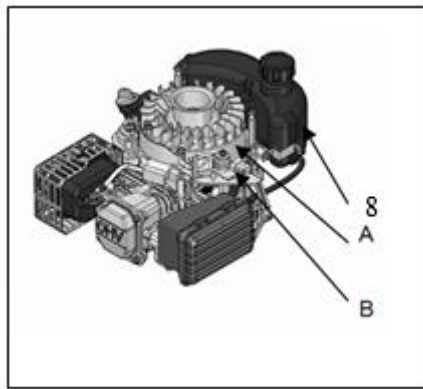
Combustível A. tanque de freio de rodas sistema B.
